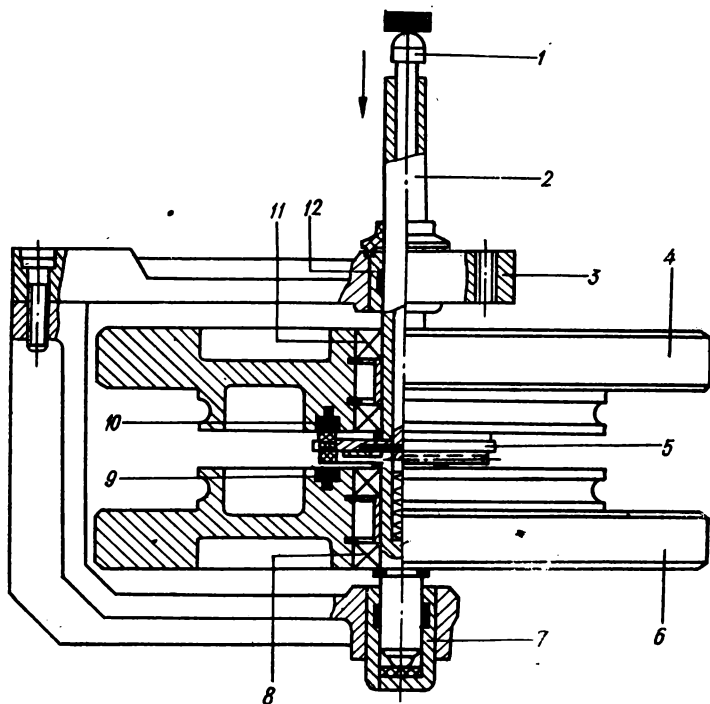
Конструкция реверсивного узла ведущего вала исполнения VI.
